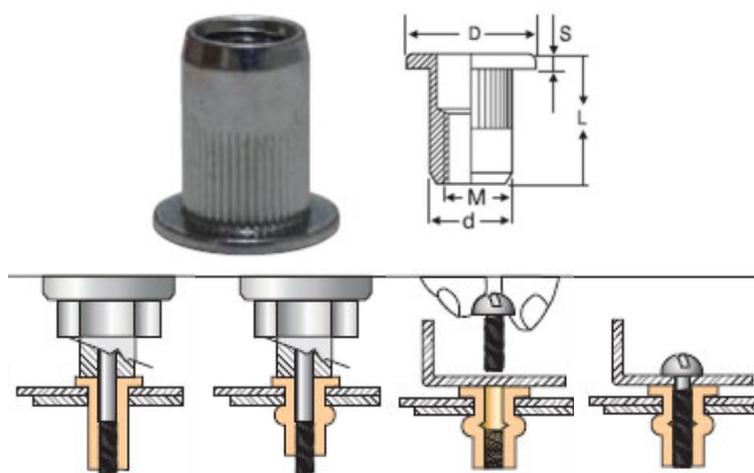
Общий вид резьбовой заклепки и принцип ее установки
